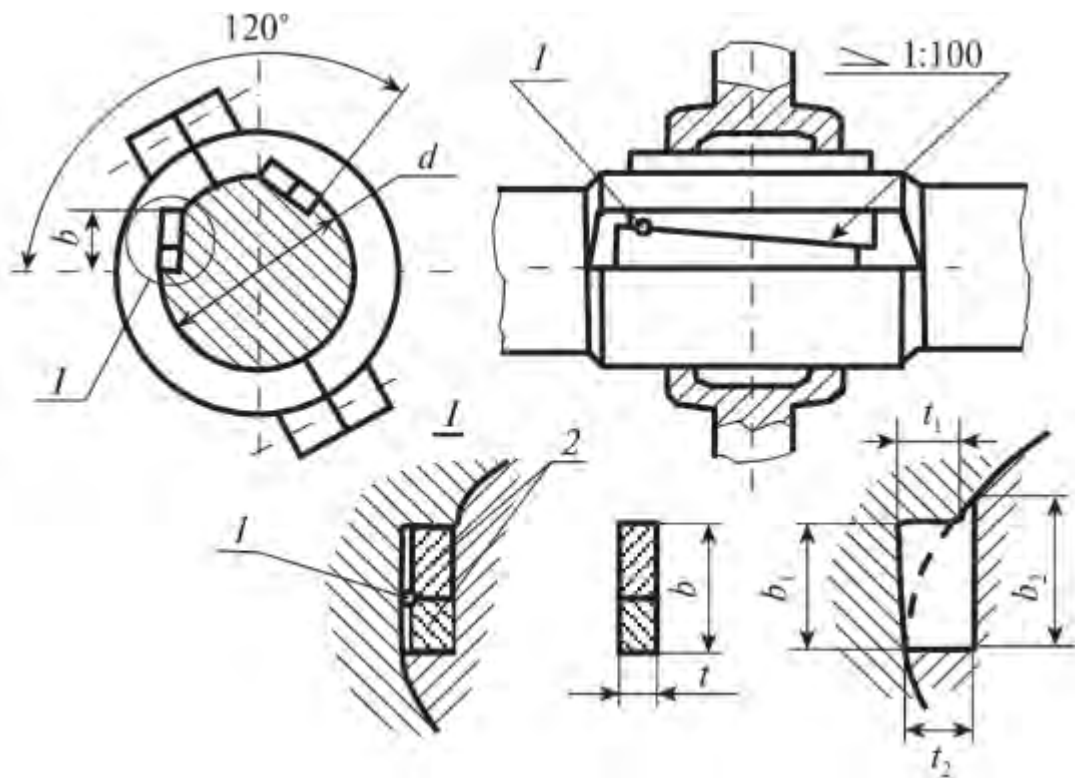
Схема шпоночного соединения с тангенциальными шпонками:
